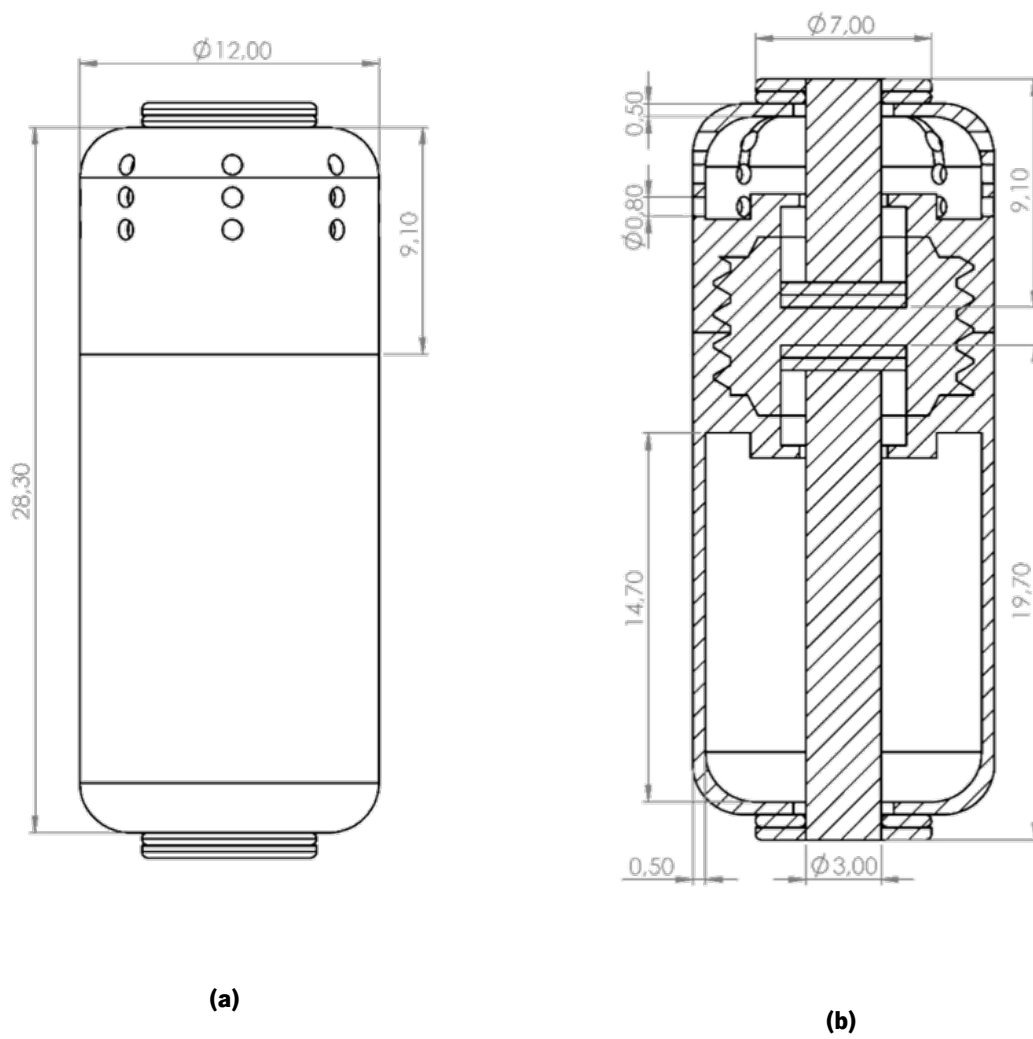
Design* CAD e dimensões (mm) do corpo da cápsula ingerível 1.0 (Disco 5 mm): a) vista lateral, b) vista em corte.
